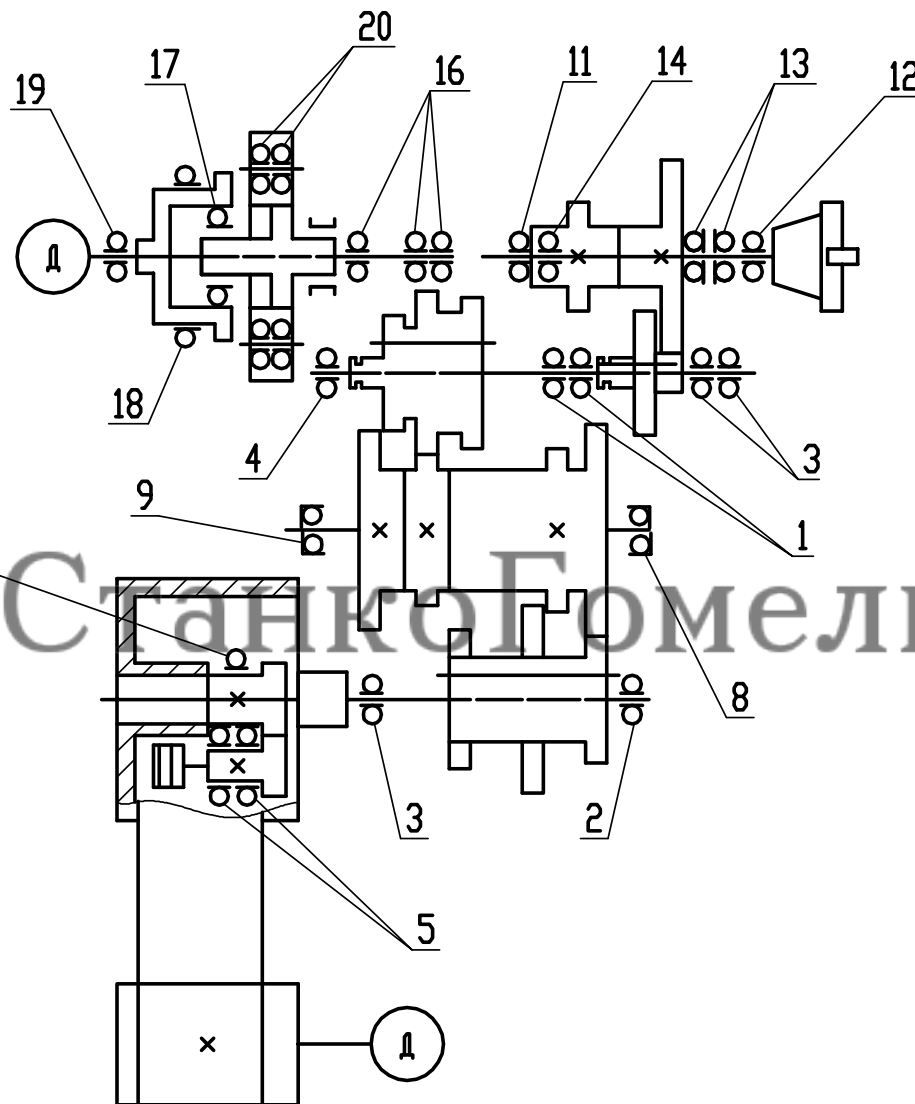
(Лист 1 из 2)- Схема расположения подшипников
